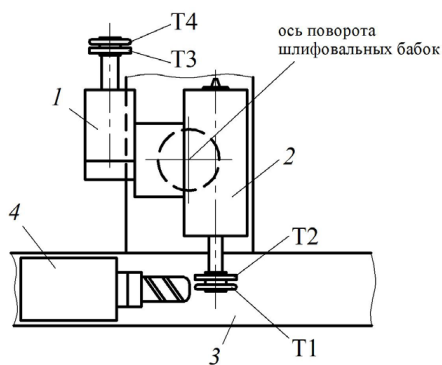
Схема установки комплекта шлифовальных кругов T1, T2, T3, T4: 1 – поворотная шлифовальная бабка; 2 – основная шлифовальная бабка; 3 – продольный стол; 4 – бабка изделия
